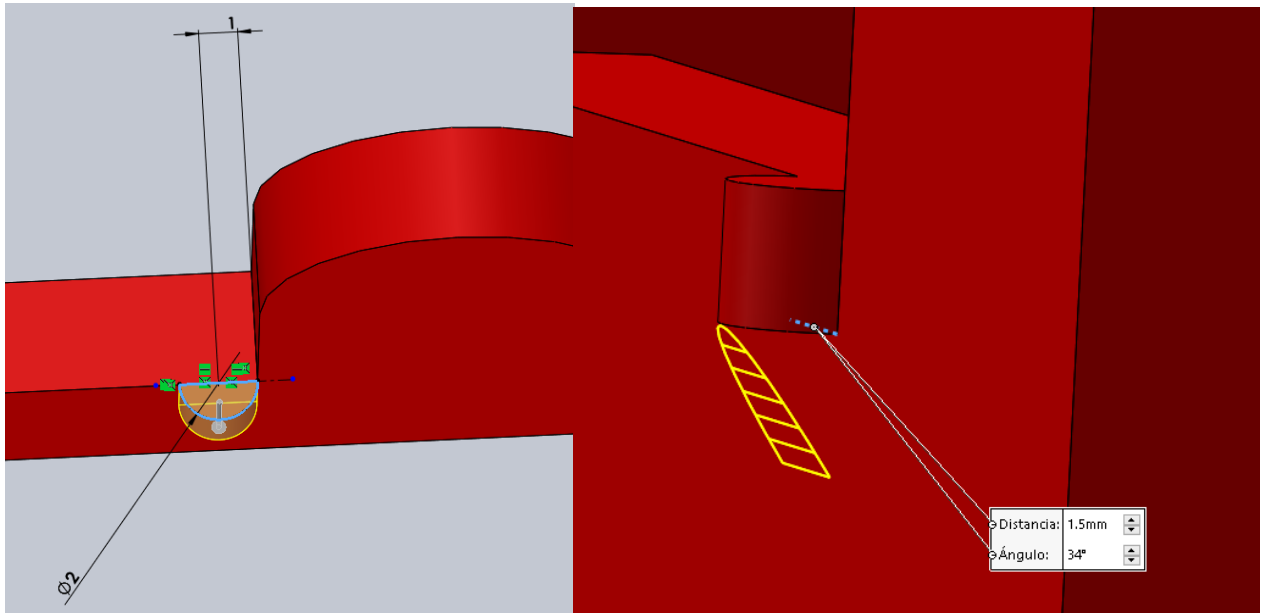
A la izquierda: construcción del resalte mediante una extrusión de 1.5mm desde su croquis. A la derecha: construcción del chaflán en su cara inferior.
